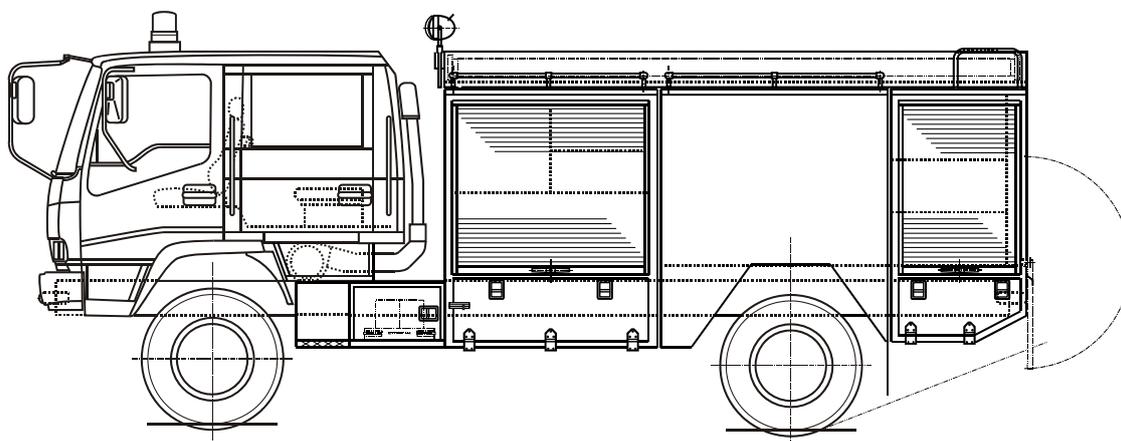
Plan de profil du fourgon pompe mousse
